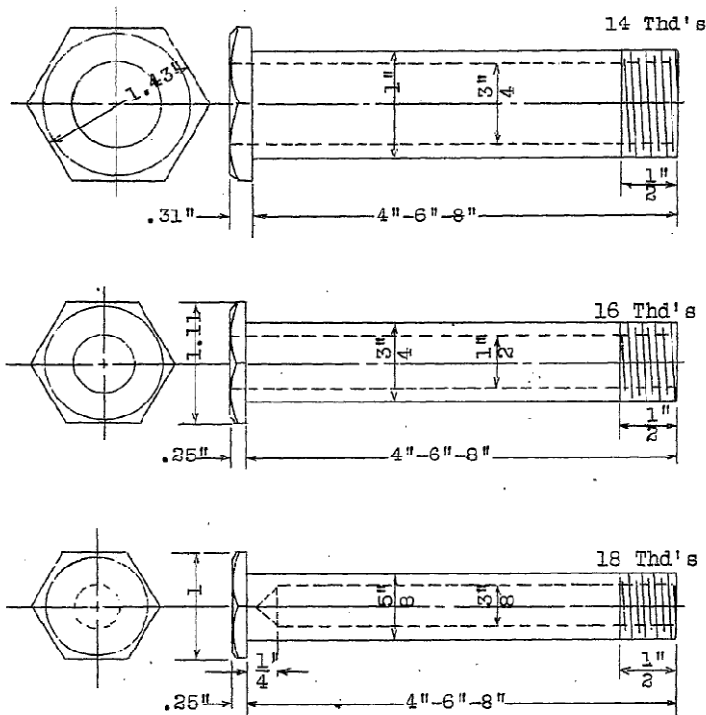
Dimension der Hohlschrauben in Zoll (Trayer, 1928)
